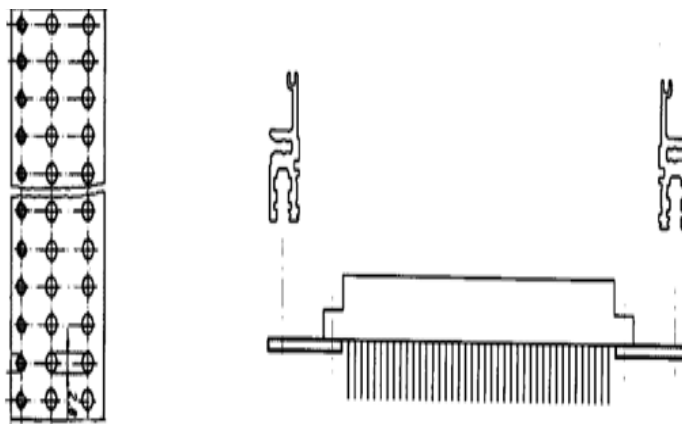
Крепление соединителя на перфорированном рельсе с резьбовыми отверстиями в субблоке типа eucoras PRO немецкой компании Schroff [48]
